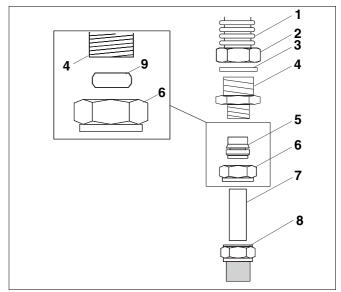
Collegamento del Twin Tube DN 20 al sistema di serraggio con anello da 18 mm
